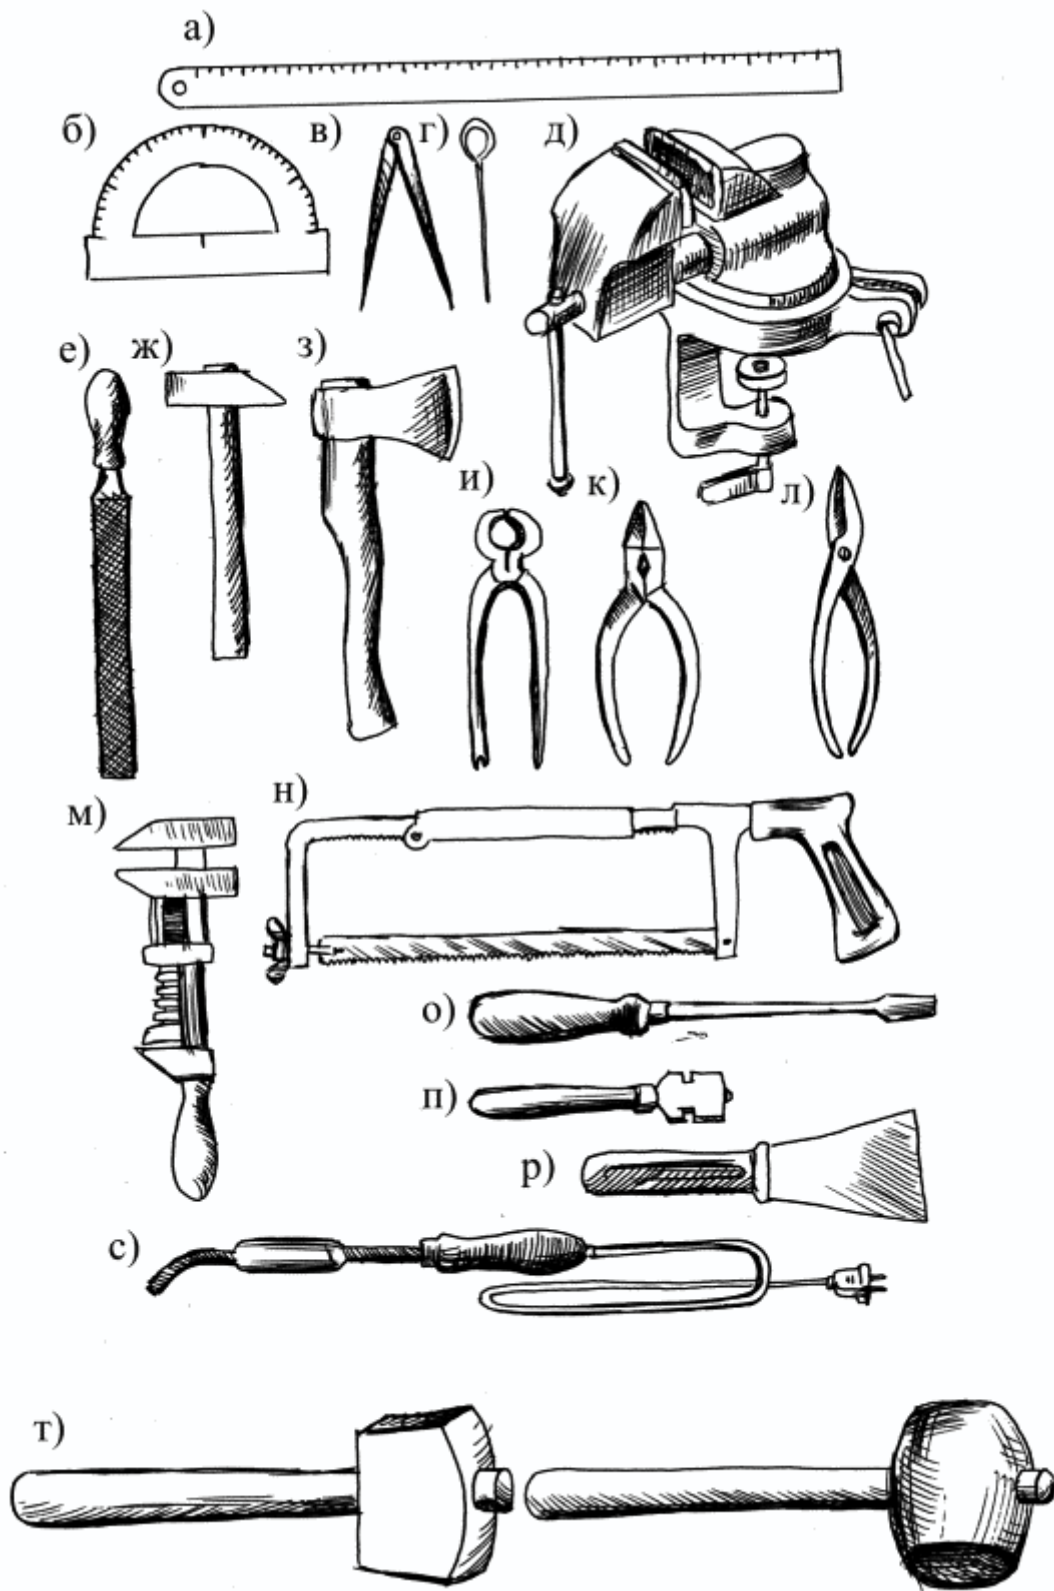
Вспомогательный инструмент: а – металлическая линейка; б – транспортир; в – циркуль; г – чертилка; д – тиски; е – драчевый напильник; ж – молоток; з – плотничный топор; и – клещи; к – плоскогубцы; л – слесарные ножницы; м – разводный ключ; н – ножовка по металлу; о – зубило; п – стеклорез; р – шпатель; с – электропаяльник; т – киянки с призматической и цилиндрической головками
